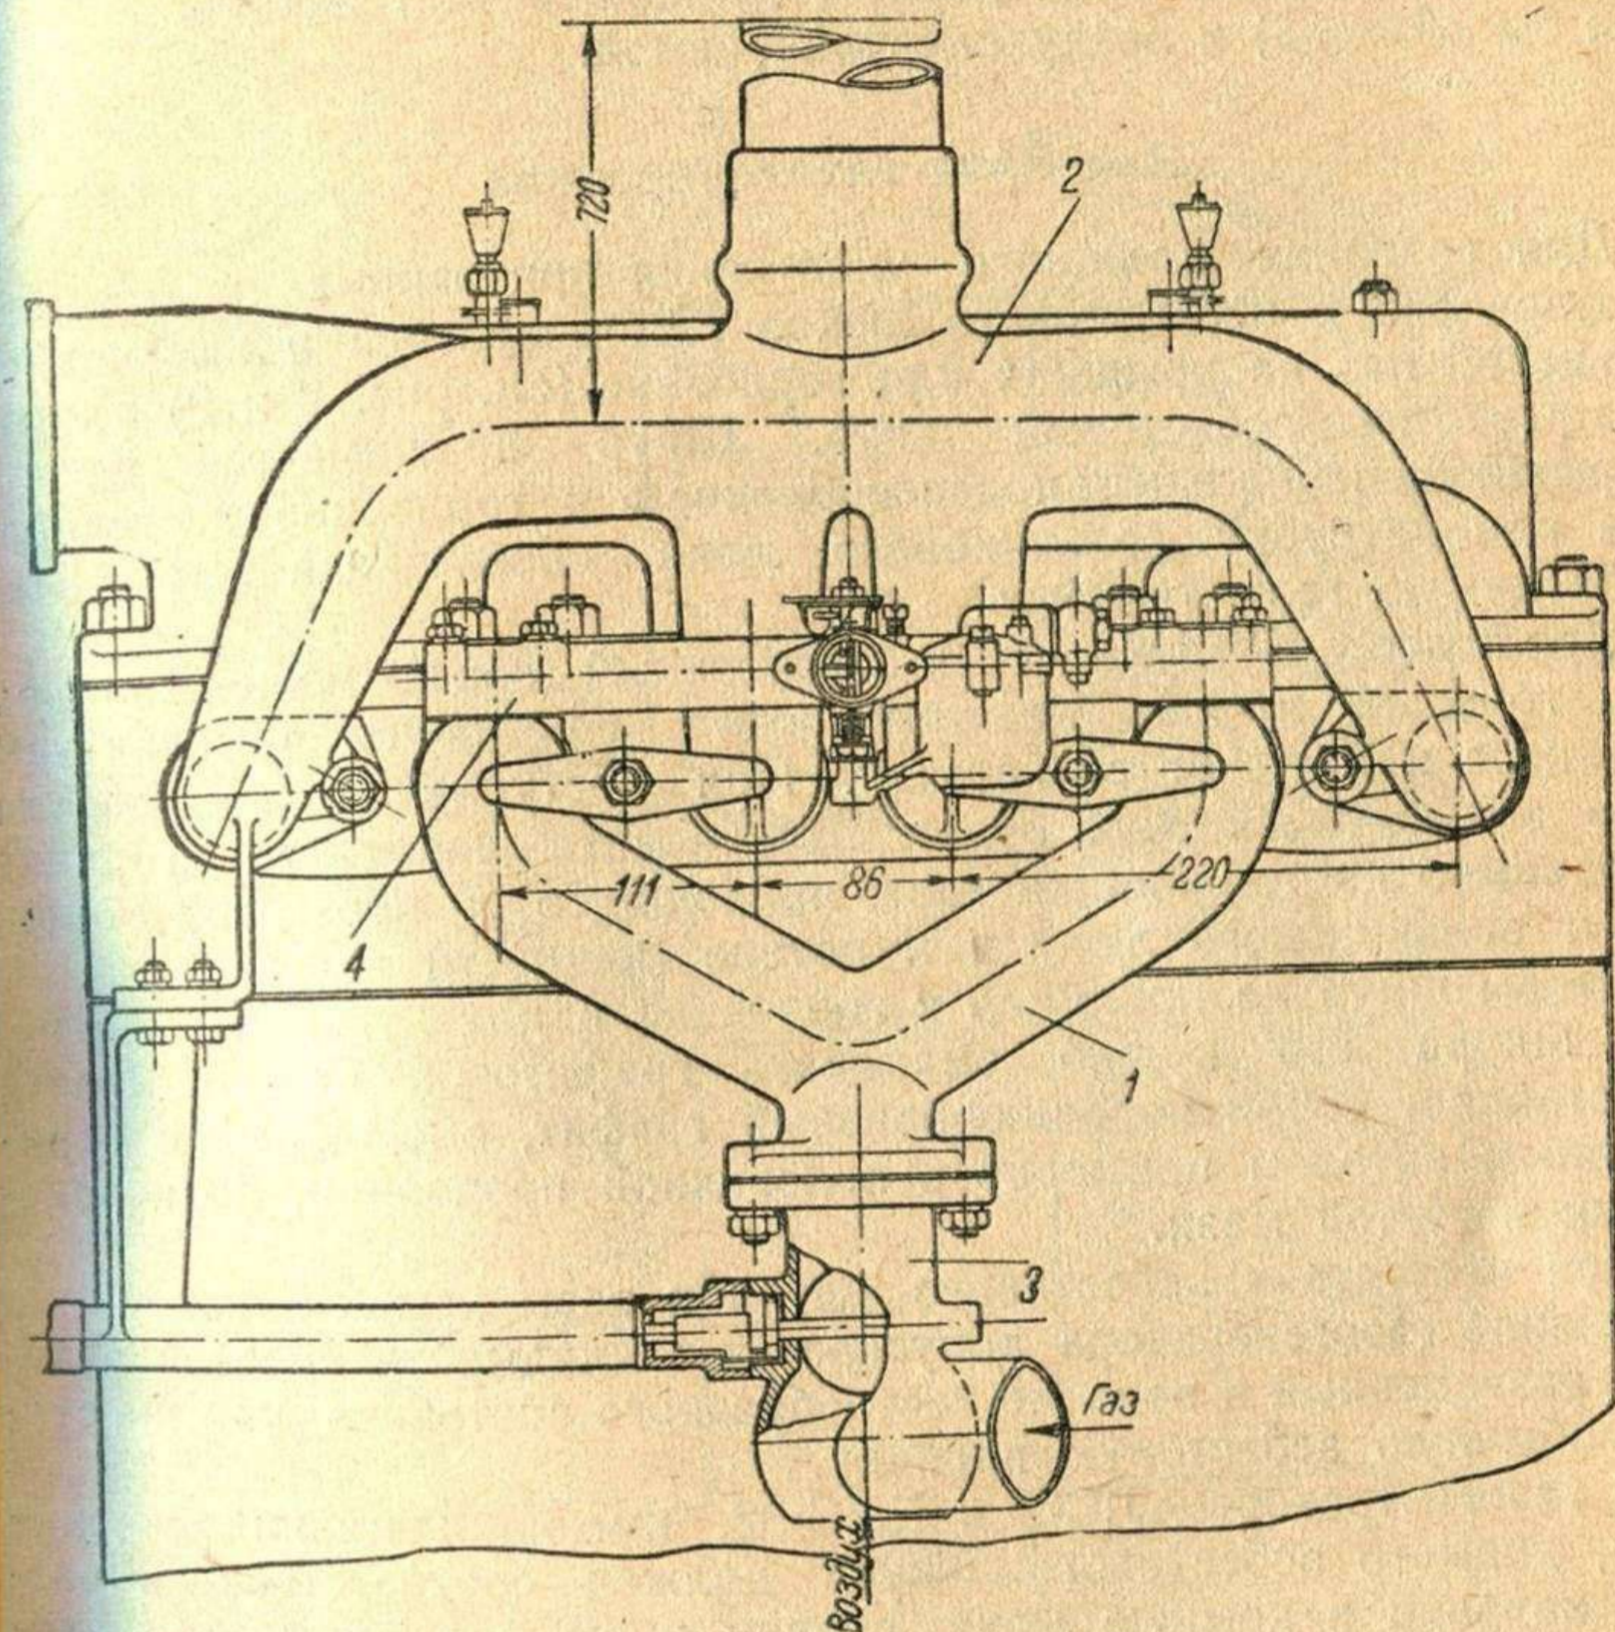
Общий вид газового двигателя СХТЗ-30:
